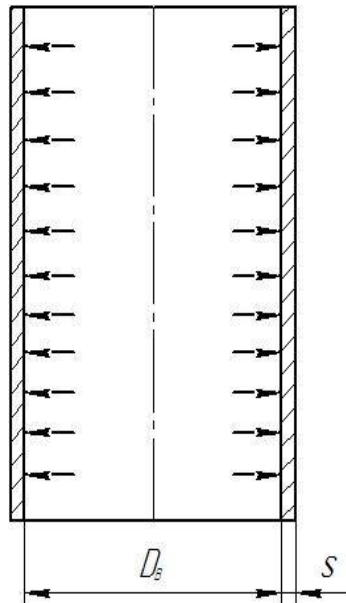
Розрахункова схема обичайки корпусу, навантаженого внутрішнім тиском
